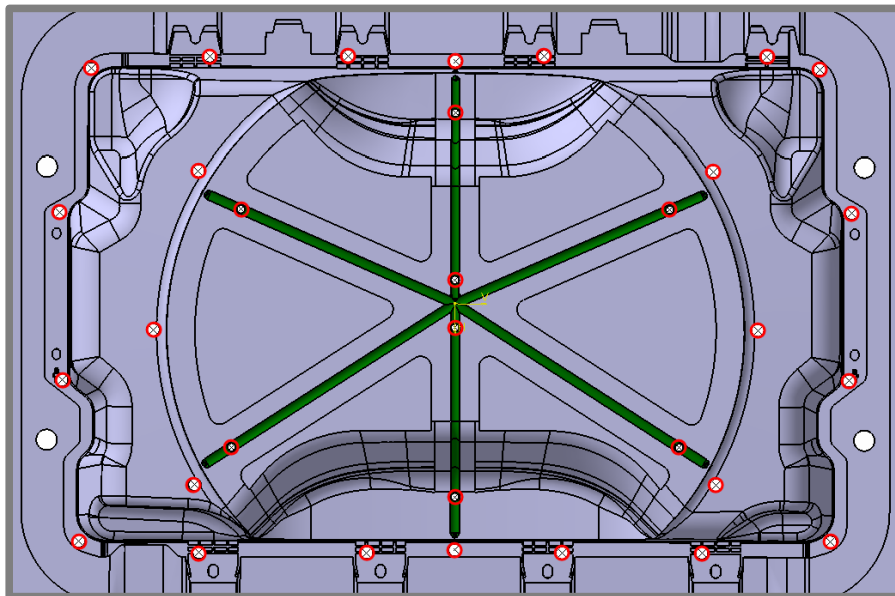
Zakrytovaná drážka pro přívodní kabel trysky
